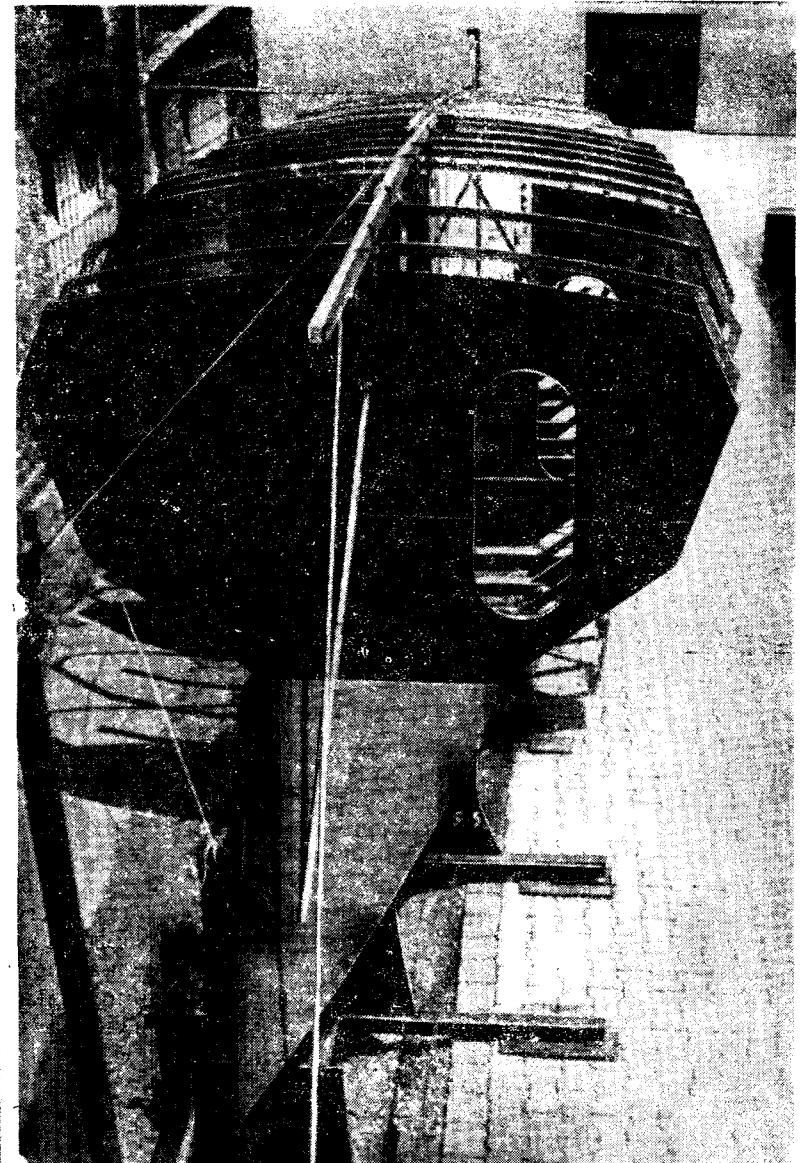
Монтаж корпуса 14-метровой яхты «Гидра» начинается с установки жесткой переборки. После угловой точечной сварки к днищевому листу переборку выравнивают строго вертикально с помощью отвеса и закрепляют одной-двумя диагональными распорками. Верхняя прочная рейка служит временной опорой, по которой выверяют шпацию для всех других шпангоутных рам и переборок.
